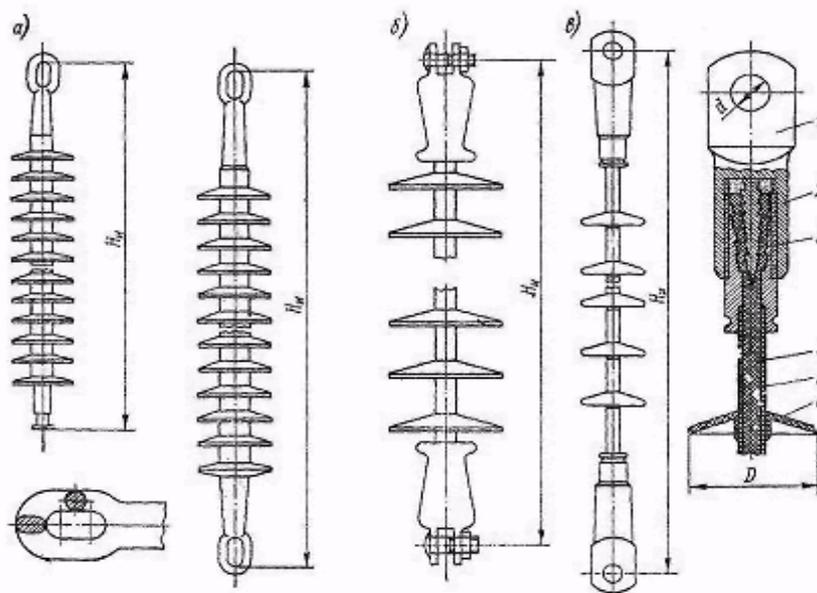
Конструкция полимерных изоляторов а) - с тарелками из этиленпропиленовых мономеров, б) - с развитой поверхностью из кремнийорганической резины, в) - конструкции ЛПИ им. М.И. Калинина с фторопластовым защитным покрытием стержня и фторопластовыми ребрами.
